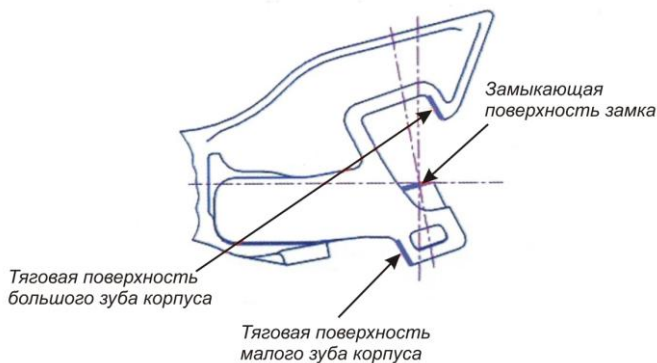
Наплавляемые поверхности зубьев корпуса и замка автосцепки СА-4
